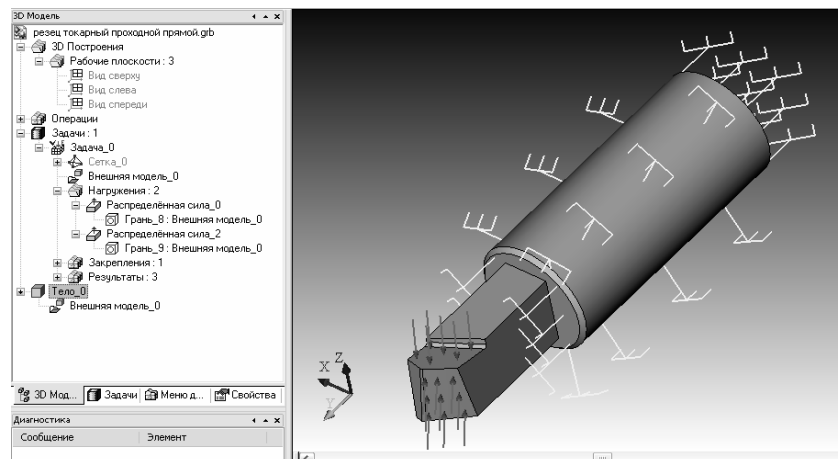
Изометрическое изображение резца в T-FLEX CAD 10
